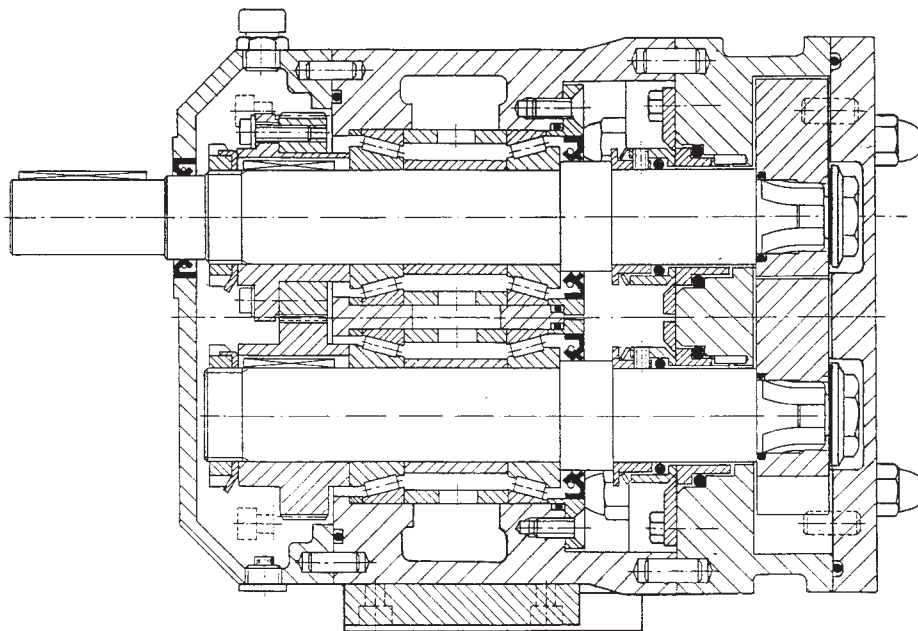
Corte transversal tipo B105 - B110 - B115
